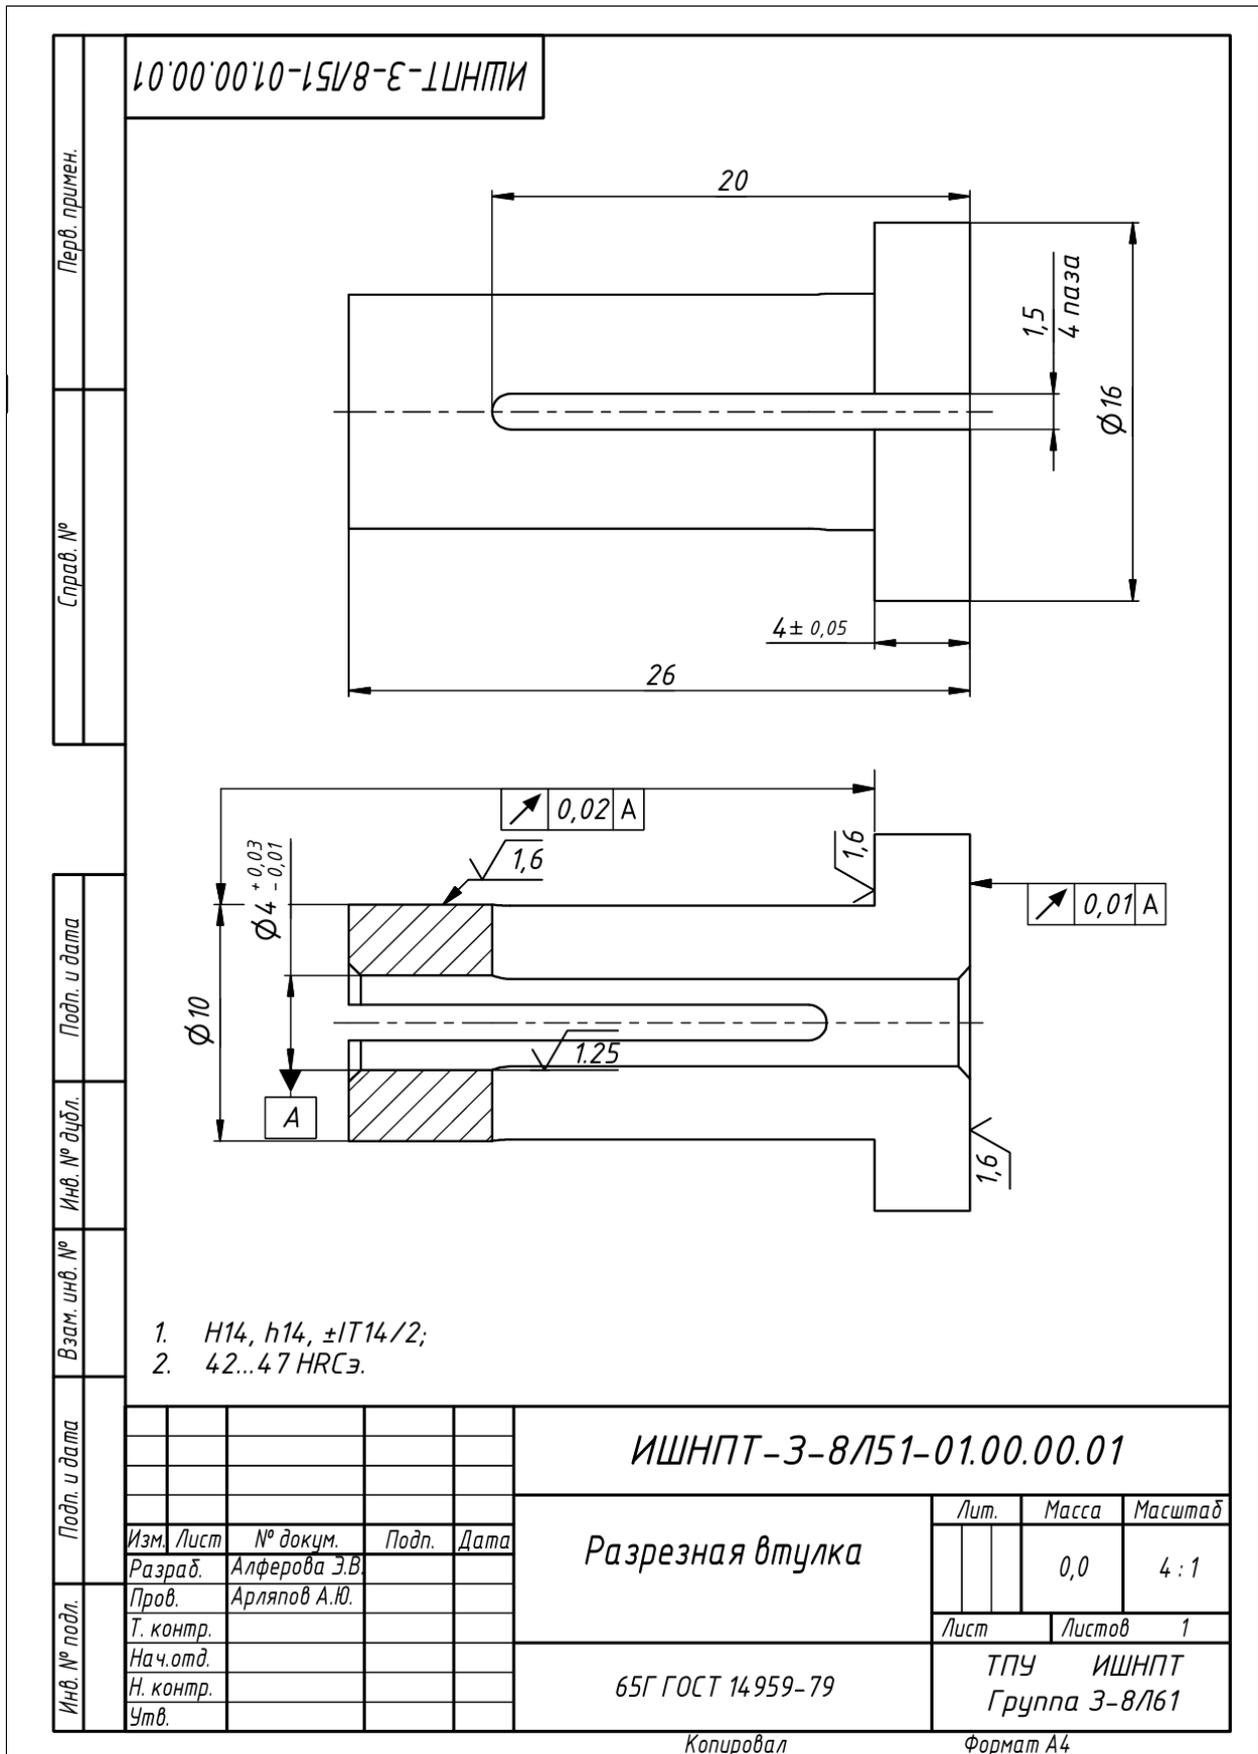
Чертеж разрезной втулки для операции фрезерная с ЧПУ.
